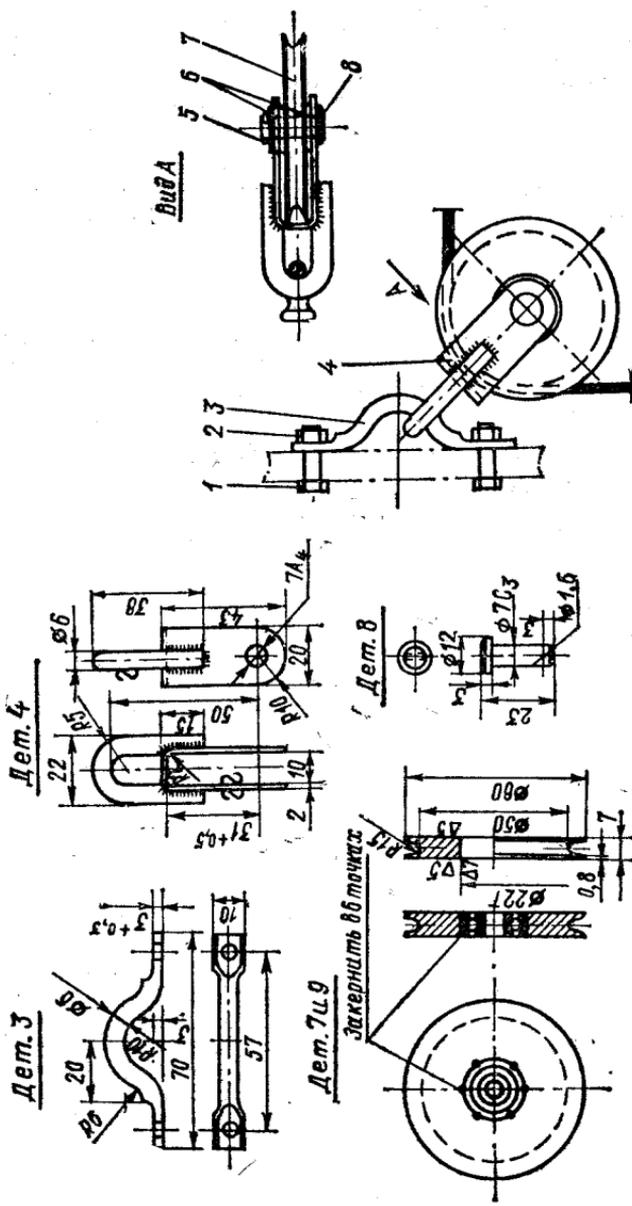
Конструкция самоустанавливающегося ролика — блока.
